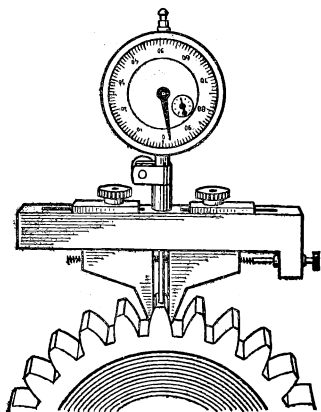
Зубомер смещения (тангенциальный зубомер)
